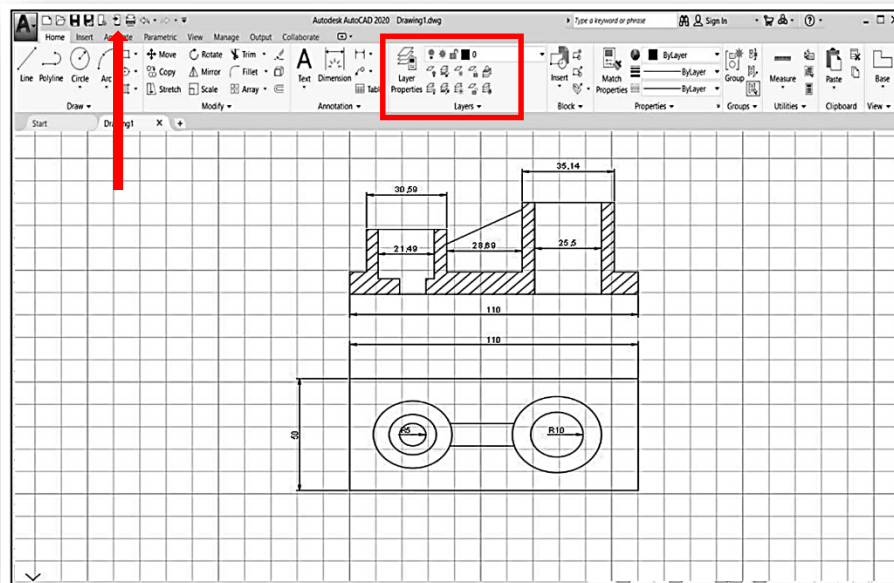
Нанесення розмірів креслення деталі
